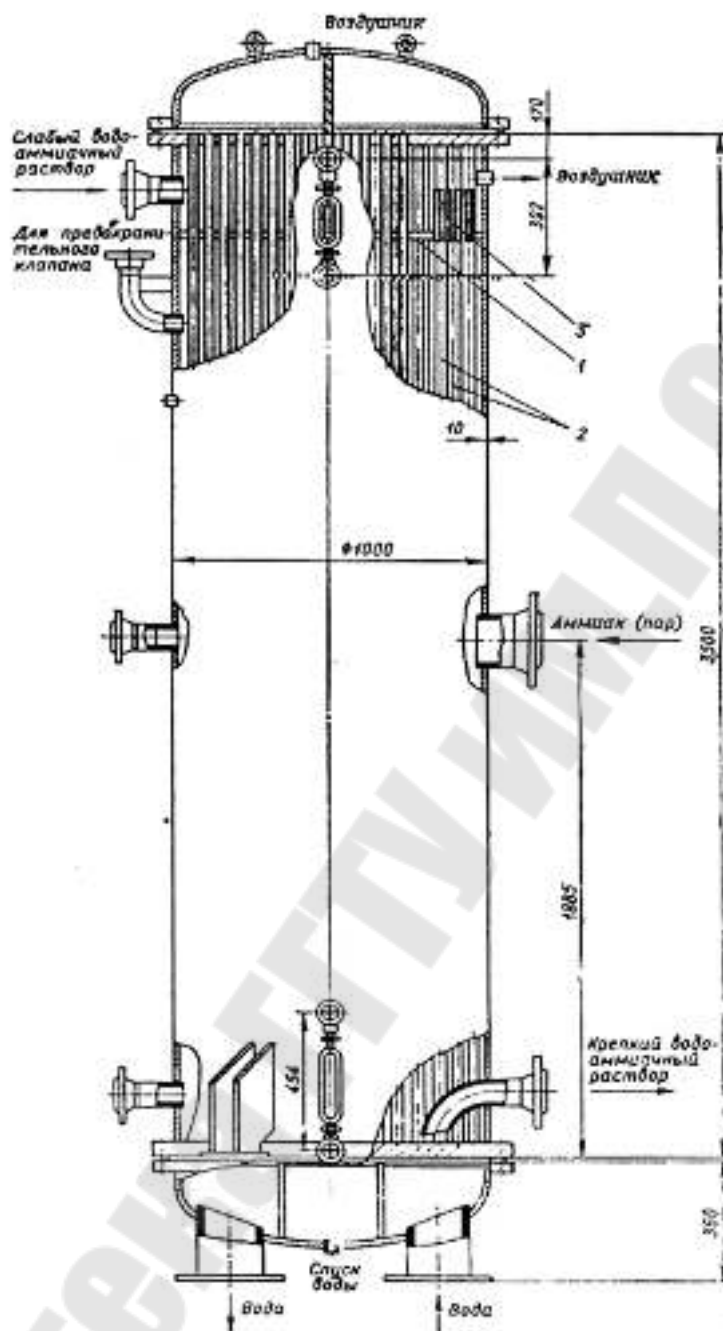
[16]. Вертикальный кожухотрубчатый абсорбер АХМ
